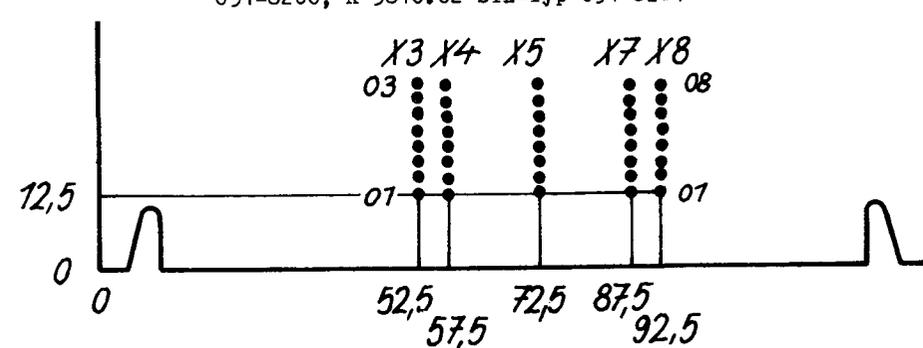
Lage der Wickelstifte auf OPS K 3510+02 STE-Typ 051-8271, K 3510.03 STE-Typ 051-8272, K 3510.04 STE-Typ 051-8273; ABS K 7010 STE-Typ 051-8300; PRZ K 0410 STE-Typ 051-8380; DAR K 9213.01 STE-Typ 051-8430, K 9213.02 STE-Typ 051-8431
